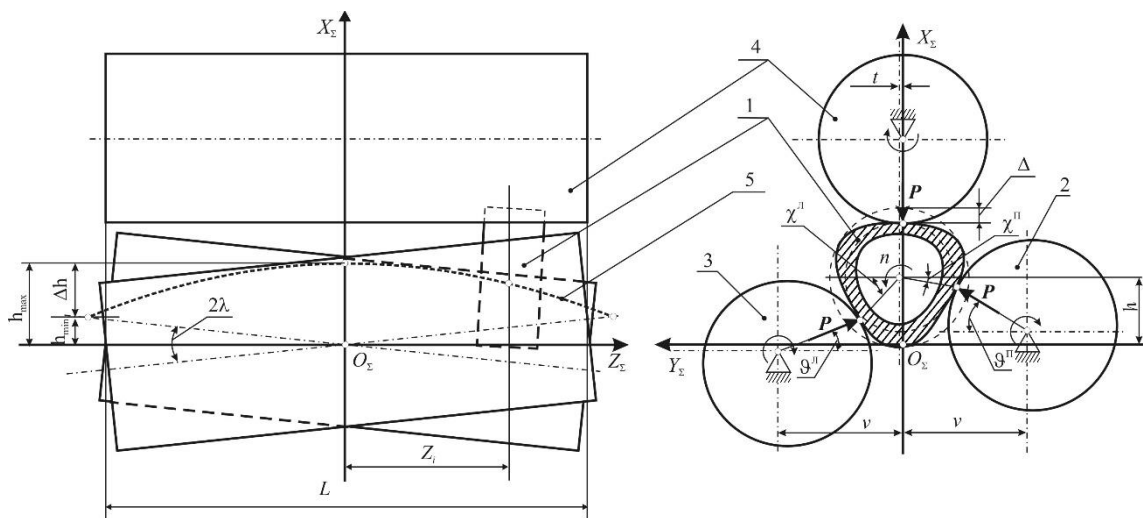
Координатная схема геометрической наладки валкового устройства: 1 – деталь; 2, 3 – базирующие валки; 4 – прижимающий валок; 5 – траектория движения детали
